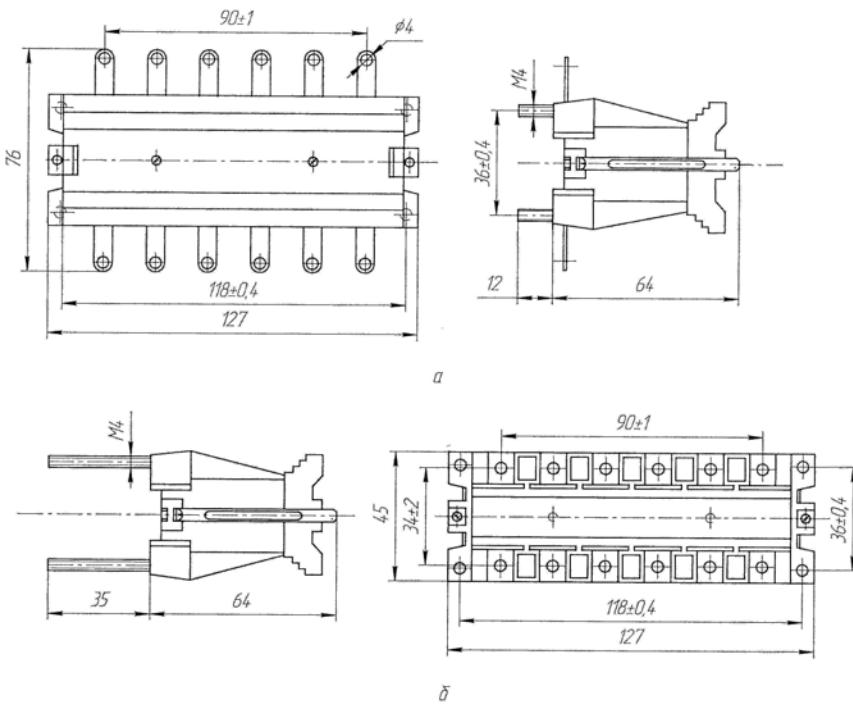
Габаритные, установочные и присоединительные размеры блока типа БИ 6М
